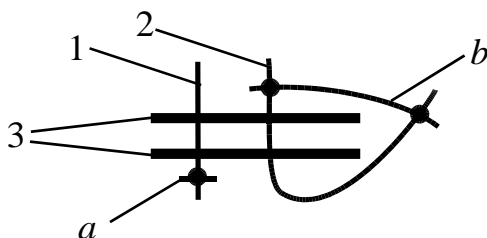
Умовне позначення чотирьохниткового зшивально-обметувального ланцюгового стібка типу 401.503: 1 – нитка голки зшивального стібка; 2 – нитка голки обметувального стібка; a – нитка петельника зшивального стібка; b – нитка петельника обметувального стібка
